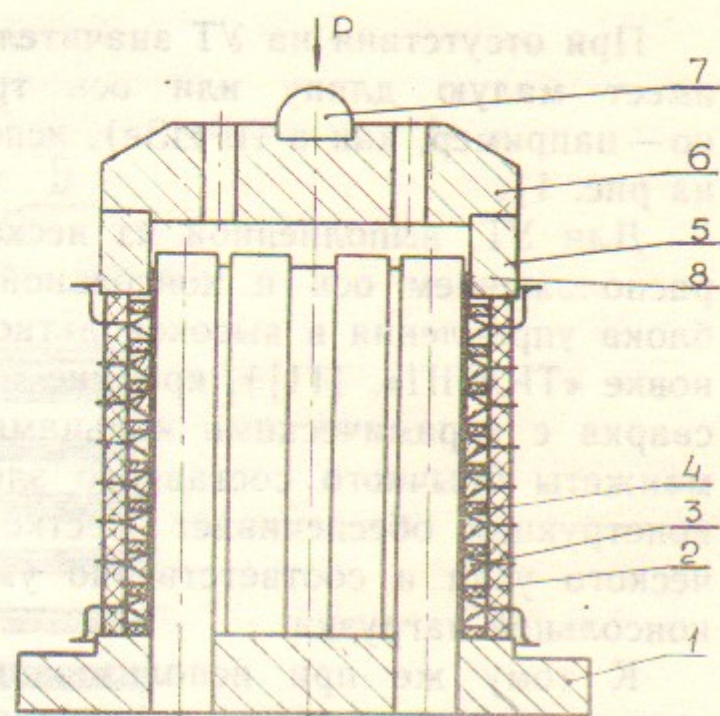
Приспособление для сварки металлокерамического изолятора:
